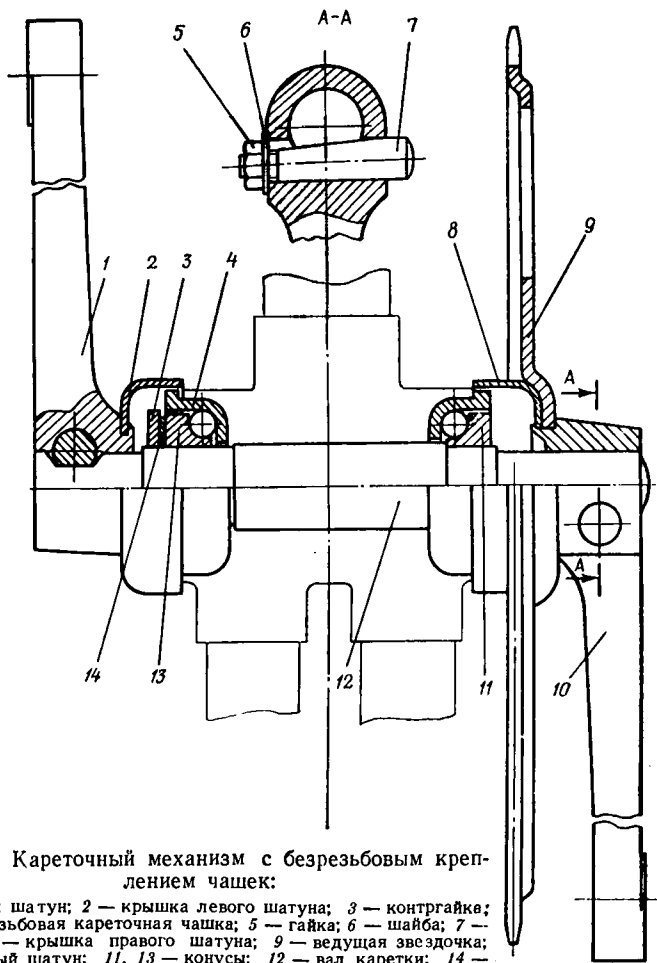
Кареточный механизм с безрезьбовым креплением чашек:
